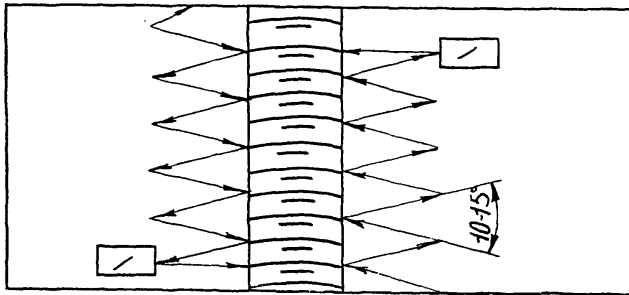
Схема перемещения искателя по поверхности при контроле сварного шва
